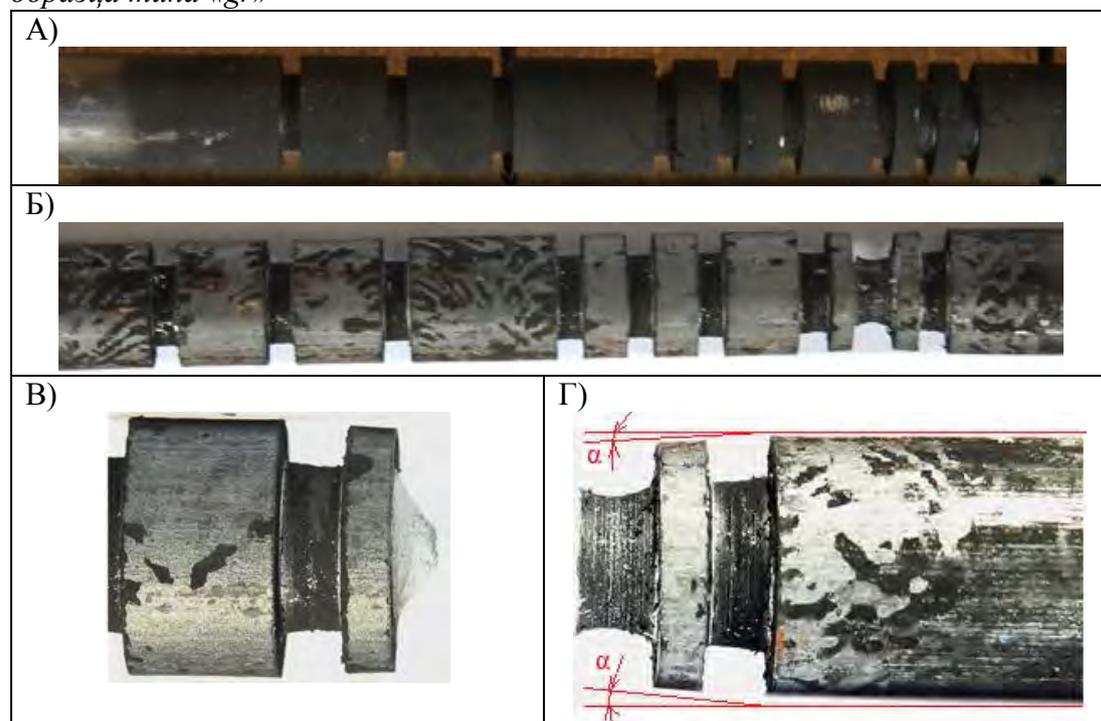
Примеры изломов в резьбовой части стержней болтов [3]: из пластичной (А) и хрупкой (Б) стали
